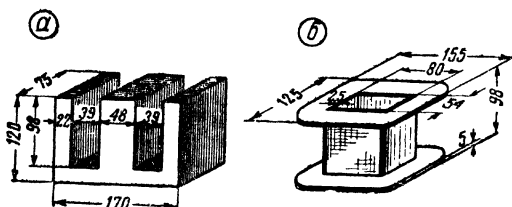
Детали дросселя размагничивающего устройства: а — сердечник; б — каркас для обмотки
